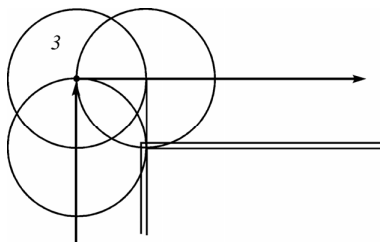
Схема отрыва и врезания инструмента при фрезеровании контура заготовки
